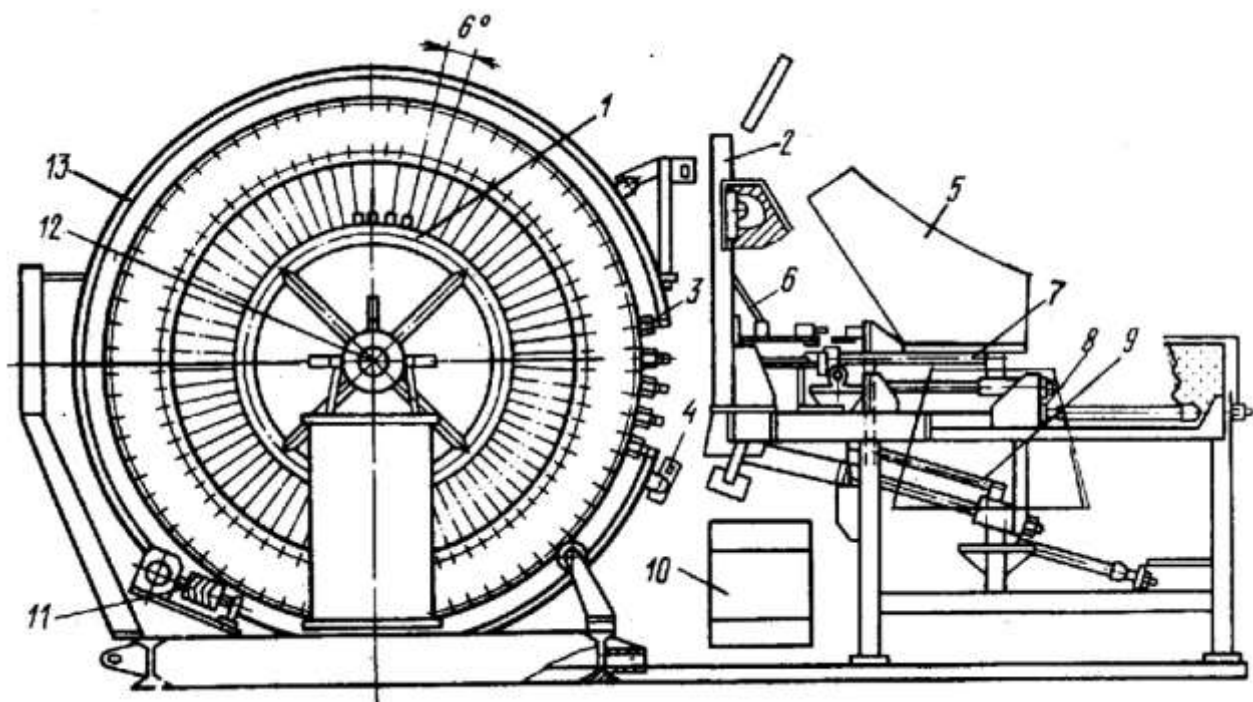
Роторный морозильный аппарат: 1 – кольцевой коллектор для подачи и отвода хладагента; 2 – щит подпрессовывающего устройства; 3 – морозильная плита; 4 – лоток; 5 – весы; 6 – подпрессовывающее устройство; 7 – механизм передвижения стола; 8 – загрузочное устройство; 9 – механизм выгрузки замороженных блоков; 10 – конвейер; 11 – привод; 12 – вал ротора; 13 – бандаж ротора
